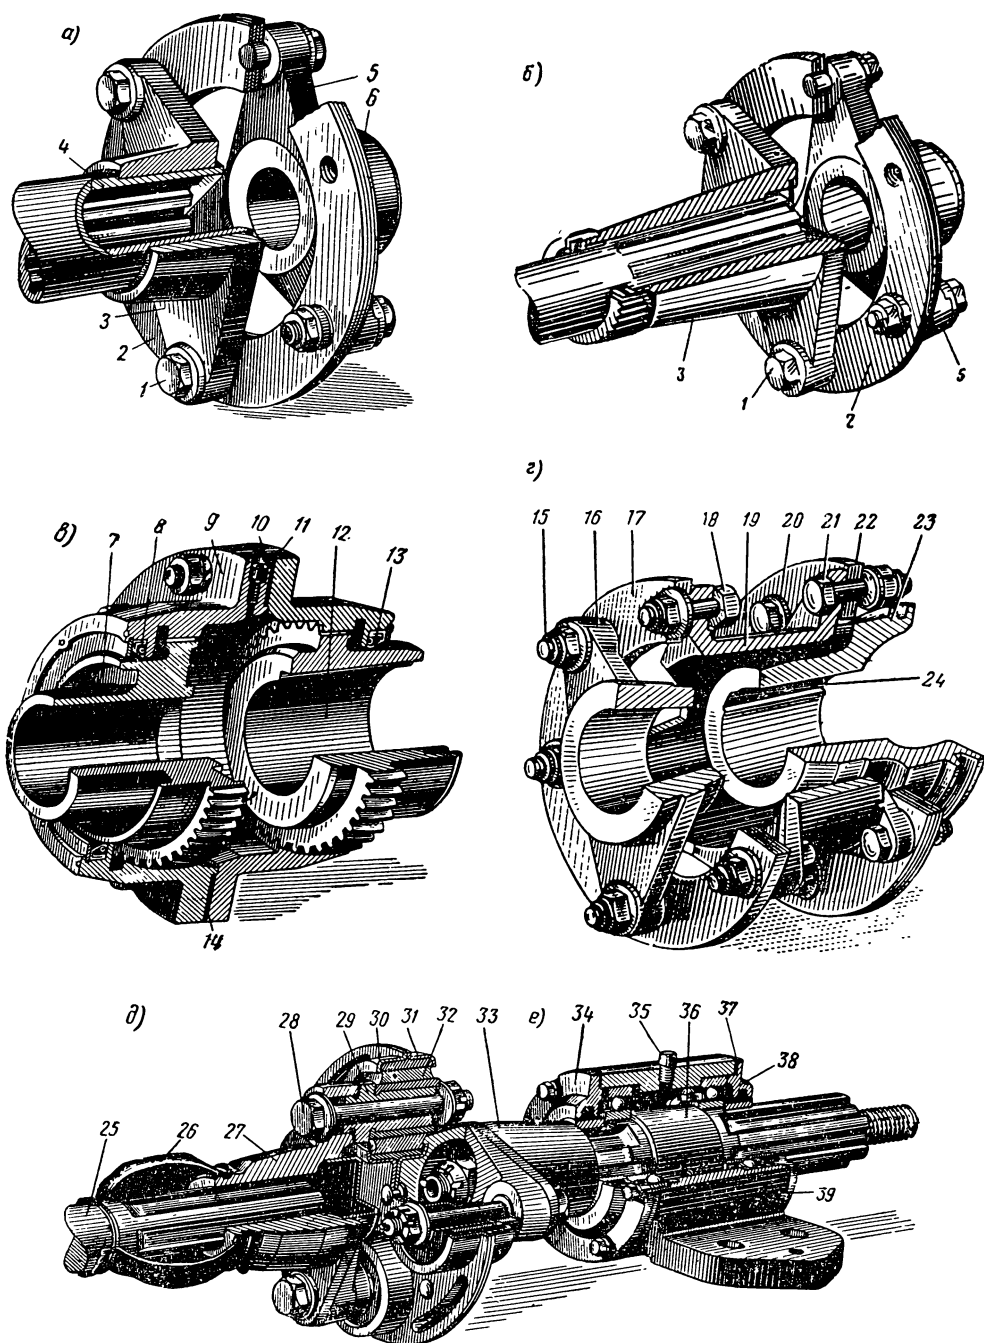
Соединительные муфты и опора подшипников привода вентилятора и компрессора:
